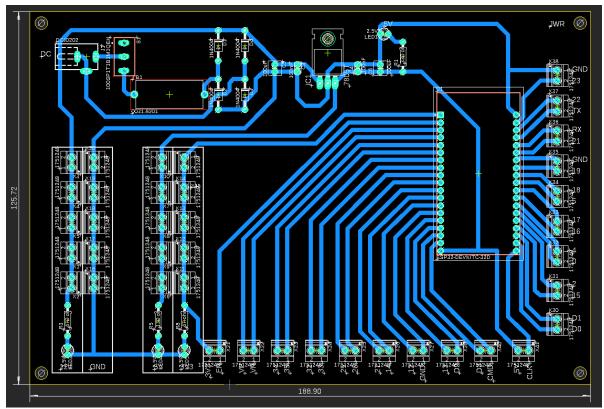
Schemat obwodu zaprojektowanej płytki PCB.
